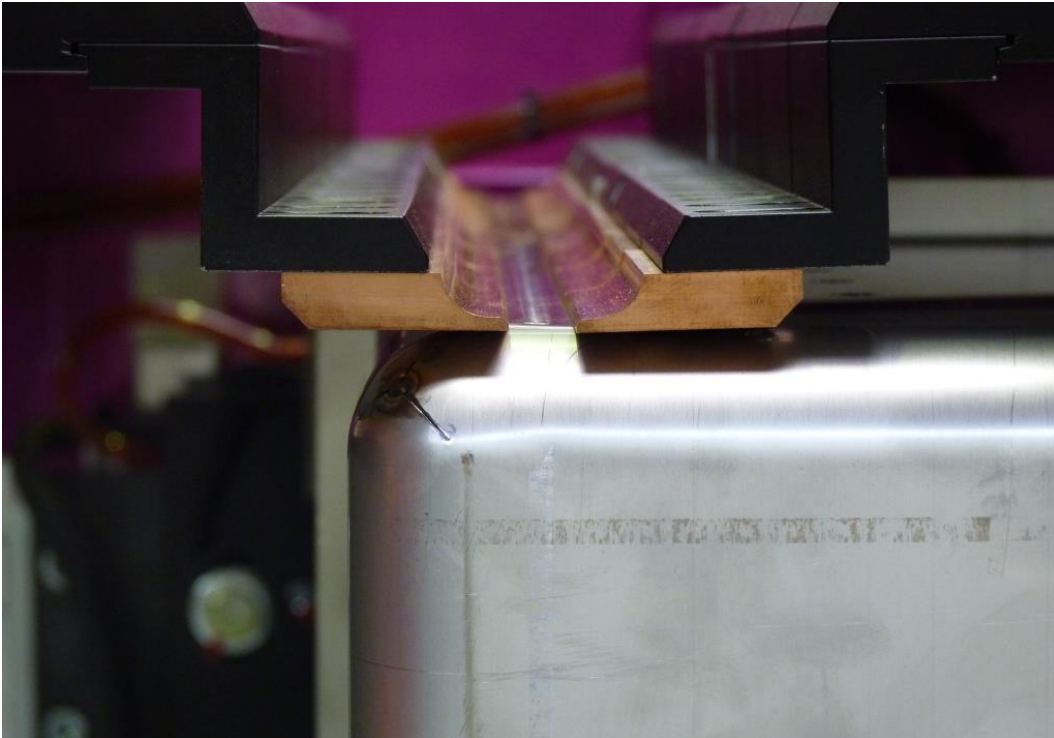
Einspannen der Box mit Präzisionsspannbacken. Die Schweißnaht ist gerade sichtbar.
